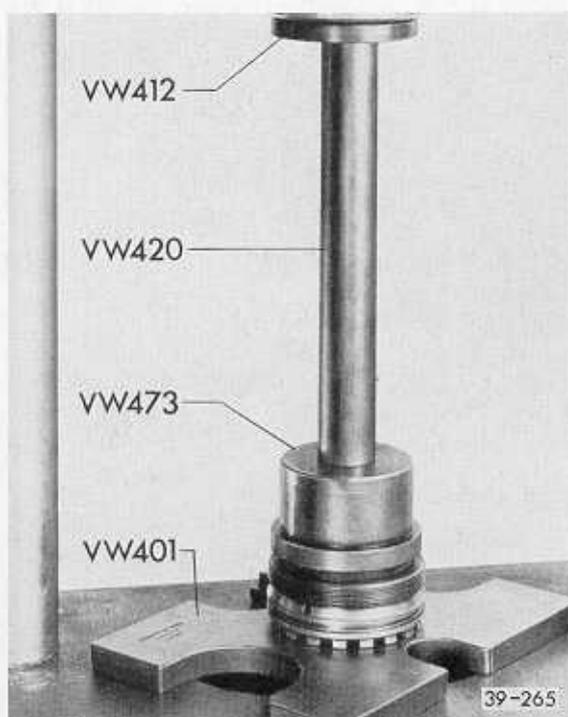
Außenring für Kegelrollenlager einpressen.
